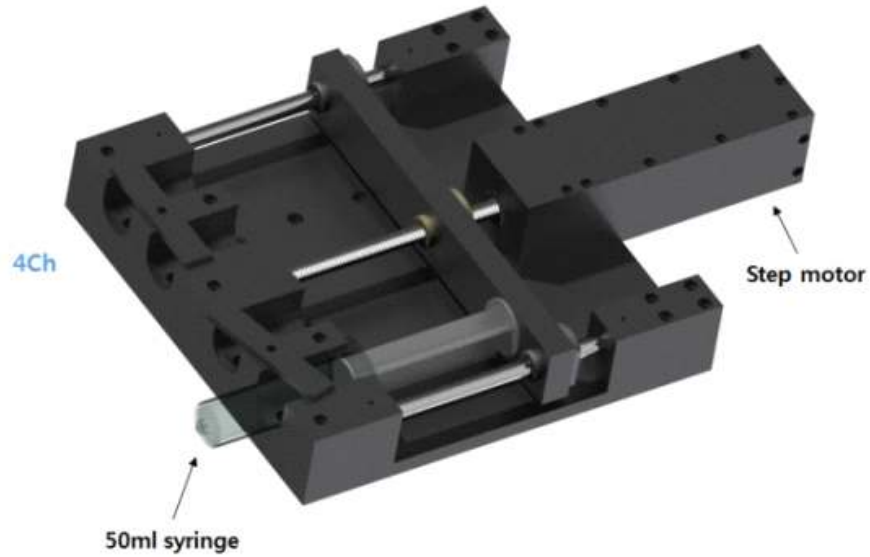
3D Tool을 이용한 syringe pump 조립성 및 가공성 확인 완료
